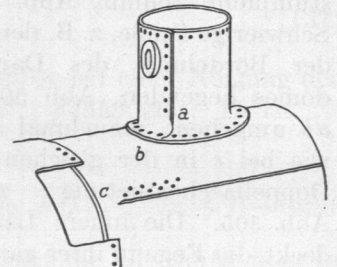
Dampfessel mit Schweißstellen bei a—b und c.
